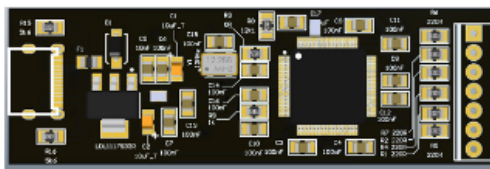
PCB del programador externo utilizado para la configuración de la FPGA.
